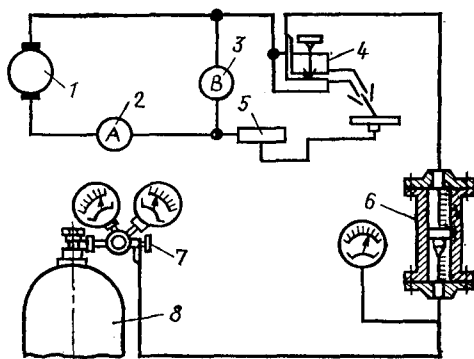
Схема аргонно-дуговой электро-сварки
